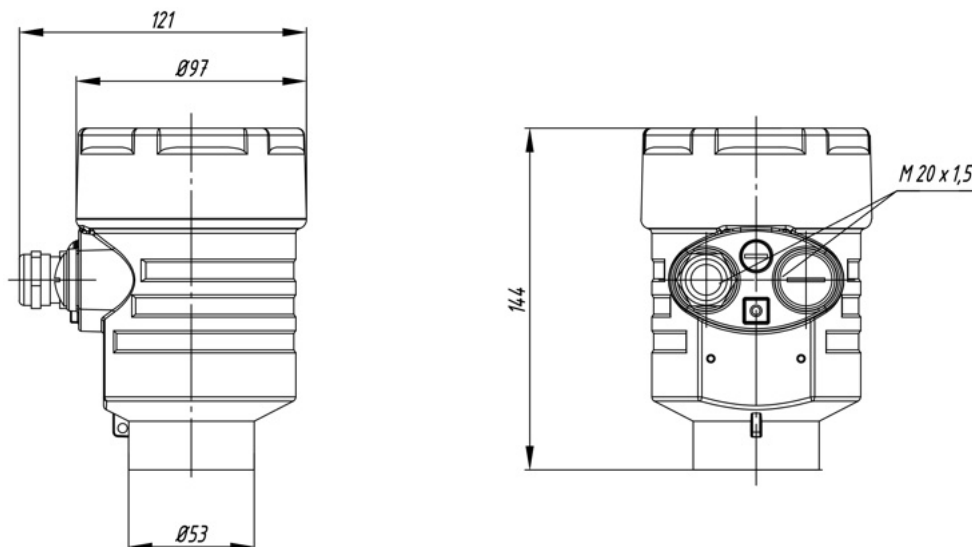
Корпус из алюминиевого сплава с 1 отсеком
